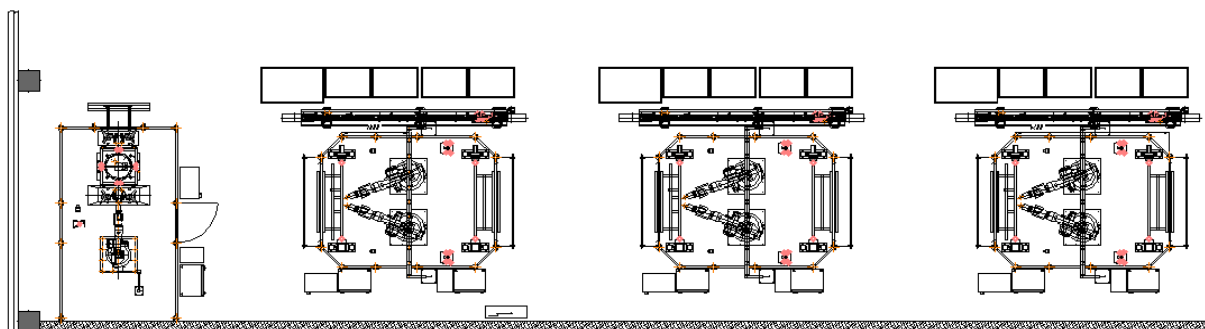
Линия сварки поперечины передней подвески на
